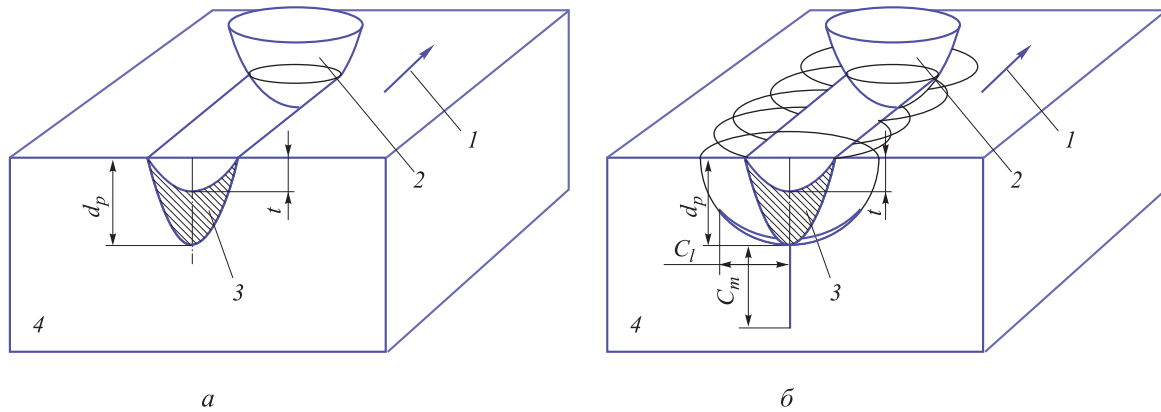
Механизмы пластического (а) и хрупкого (б) разрушения материала при алмазном шлифовании: 1 — направление шлифования; 2 — алмазное зерно; 3 — пластически деформированная зона; 4 — заготовка
